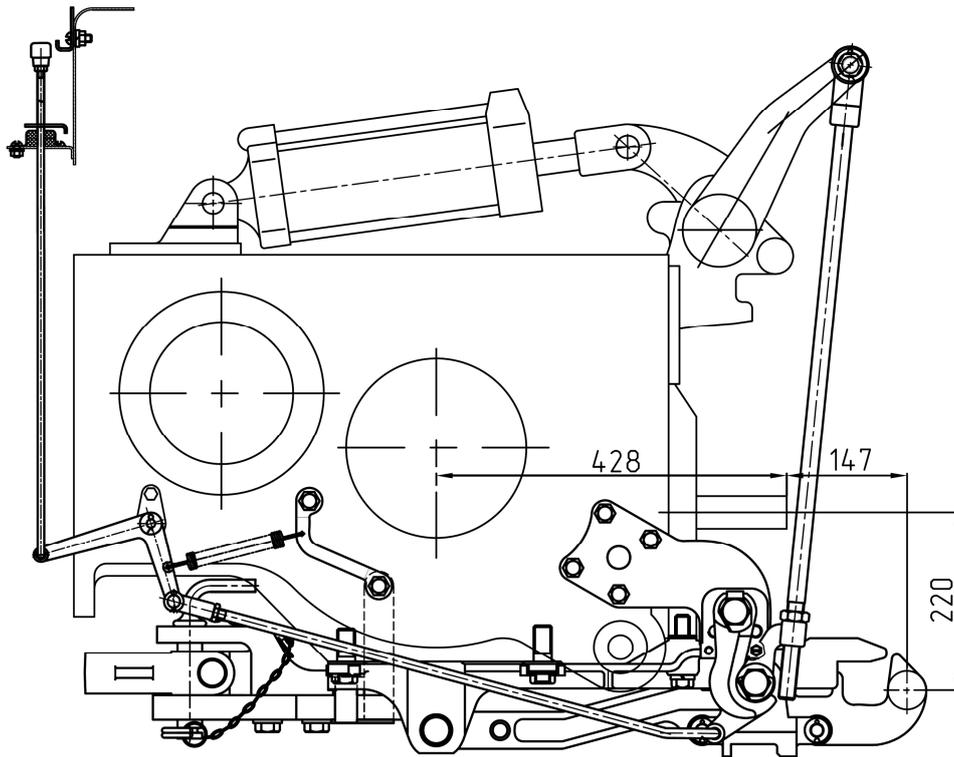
Schéma d'installation du dispositif TSU-2 (crochet hydraulique) et TSU-2M-02 (avec le crochet hydraulique installé dans la position de fonctionnement)
